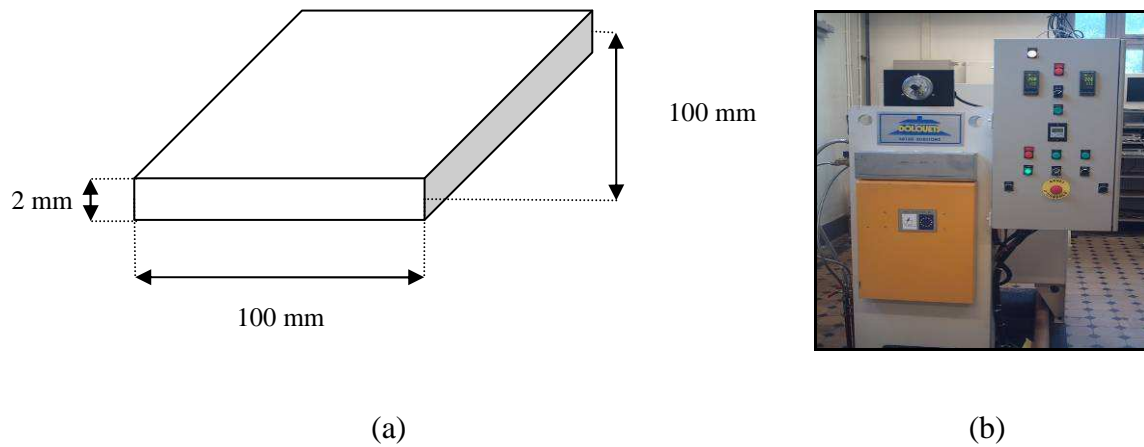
Dimension des plaques (a) et presse à plateaux chauffants (b)
